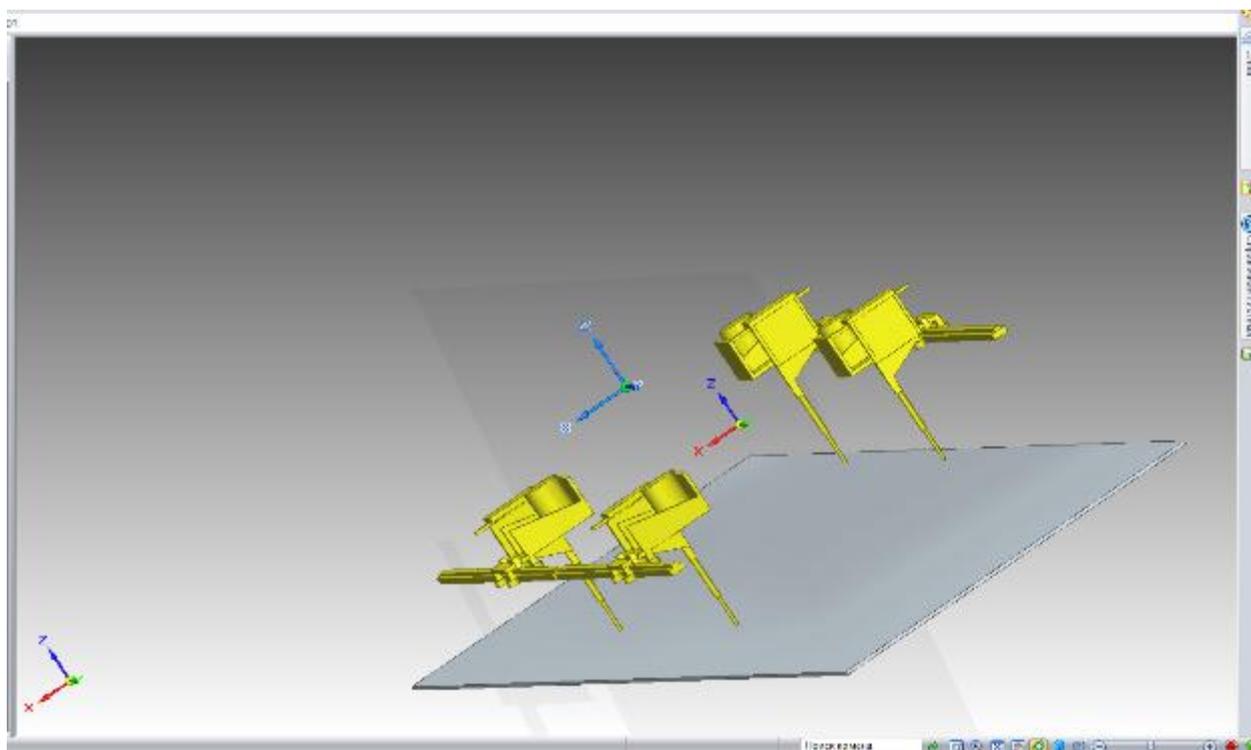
Сборка “Станция резки металла” в Solid Edge
